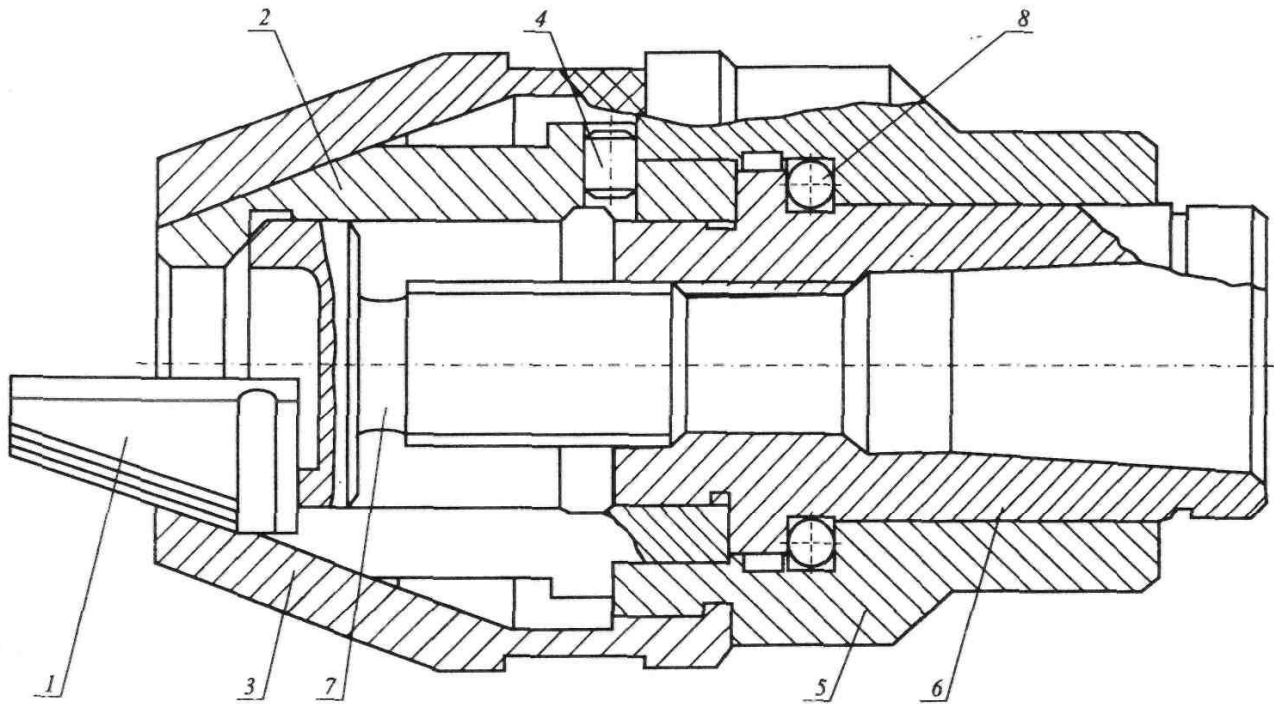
Патрон свердлильний безключовий: 1 – кулачки (3 шт.); 2 – обойма; 3 – гайка; 4 – штифт; 5 – втулка; 6 – корпус; 7 – головка з лівою різьбою; 8 – кульки.
